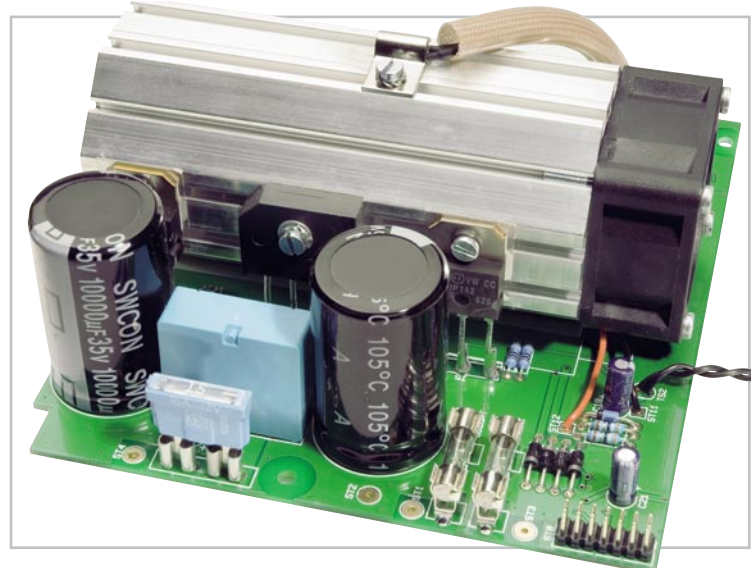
Die Befestigung der Bauteile am Kühlkörper (Ansicht linke Kühlkörperseite)
